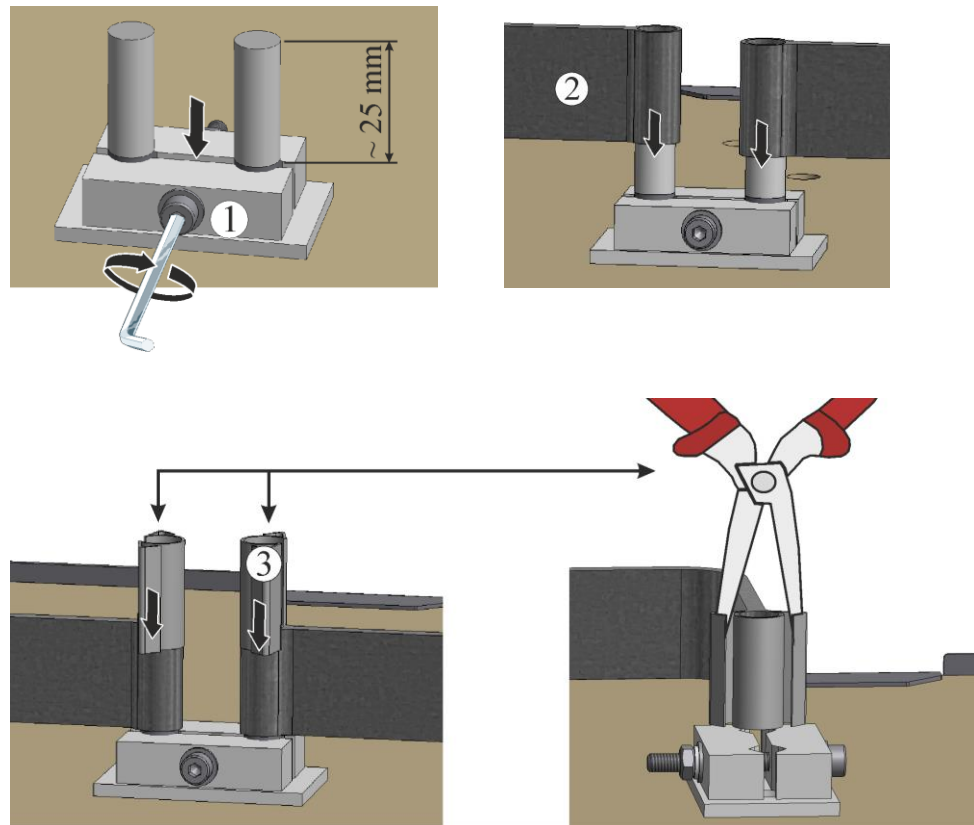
Montarea elementelor de încălzire (figură similară)
